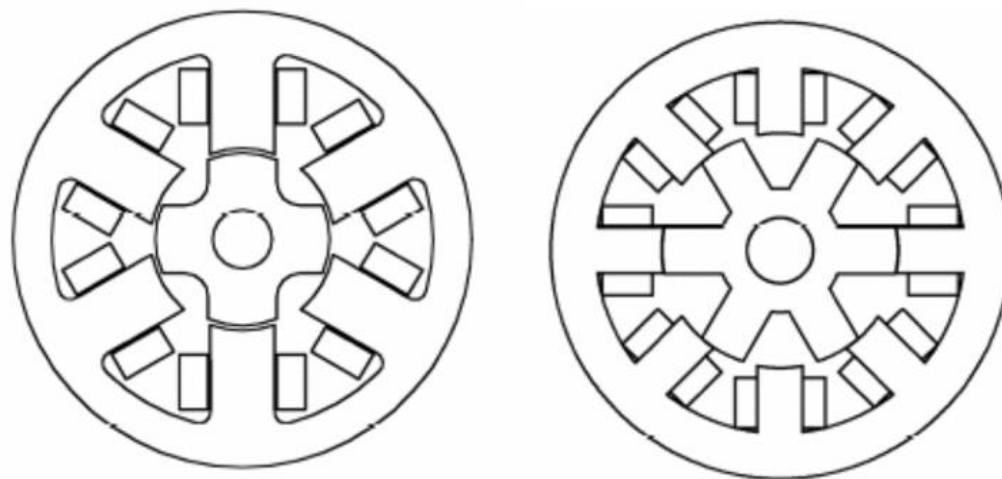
Конструкция вентильного индукторно-реактивного двигателя с 6-ю и 8-ю полюсами статора
